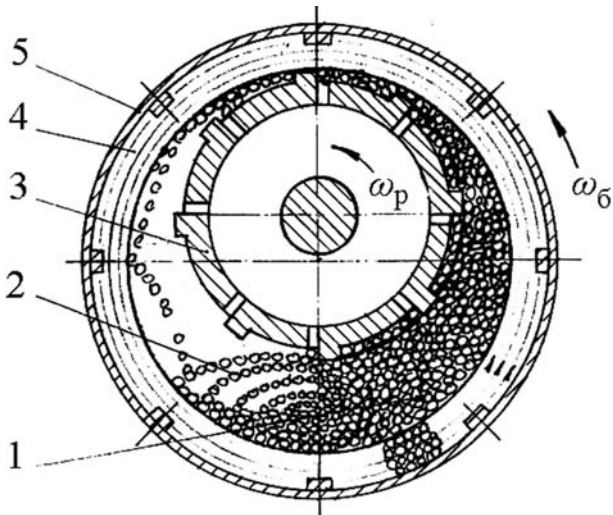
Поперечний розріз барабана ресурсозберігаючого млина примусового самоподрібнювання МПС(Р): 1 – клиновидна зона; 2 – шар обвалювання; 3 – обертальний перфорований циліндр; 4 – центрифугувальний шар; 5 – барабан
